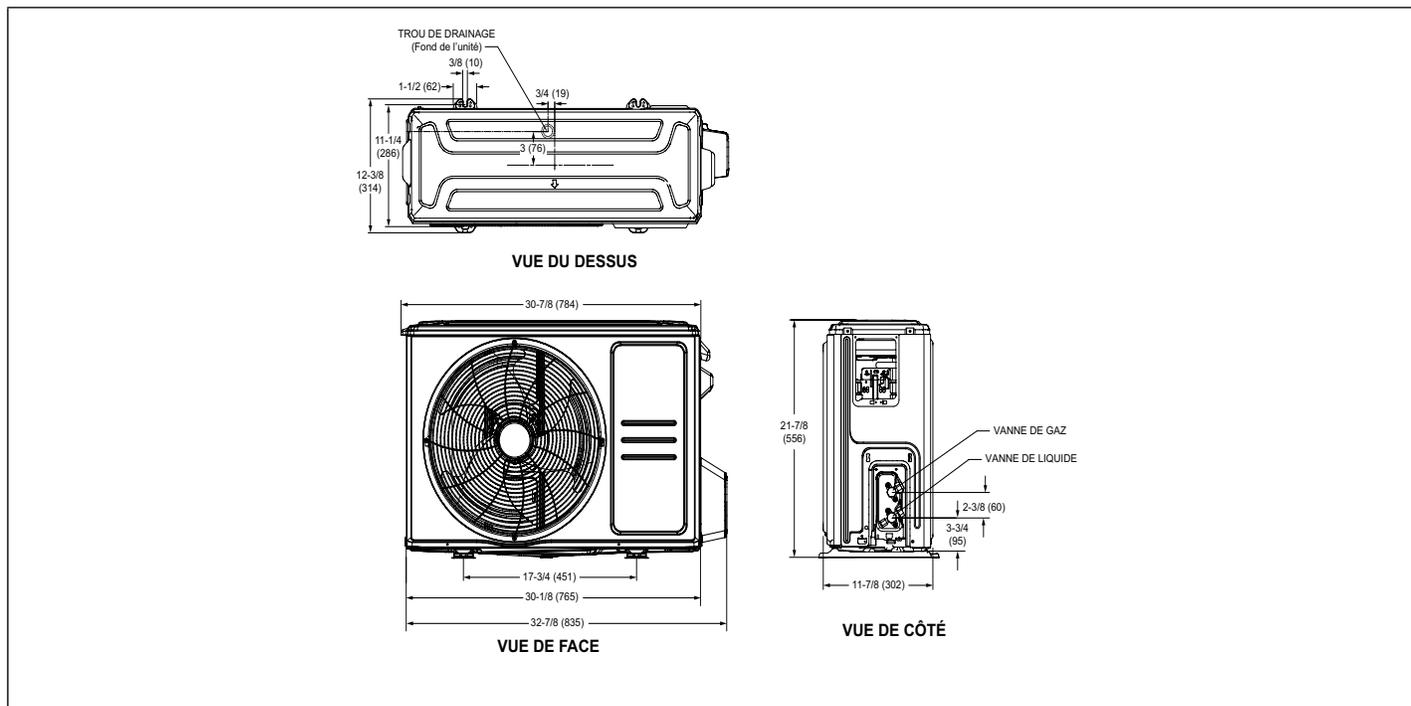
208/ 230 V - MPC012S4S - Dimensions de l'unité extérieure - pouces (mm)
